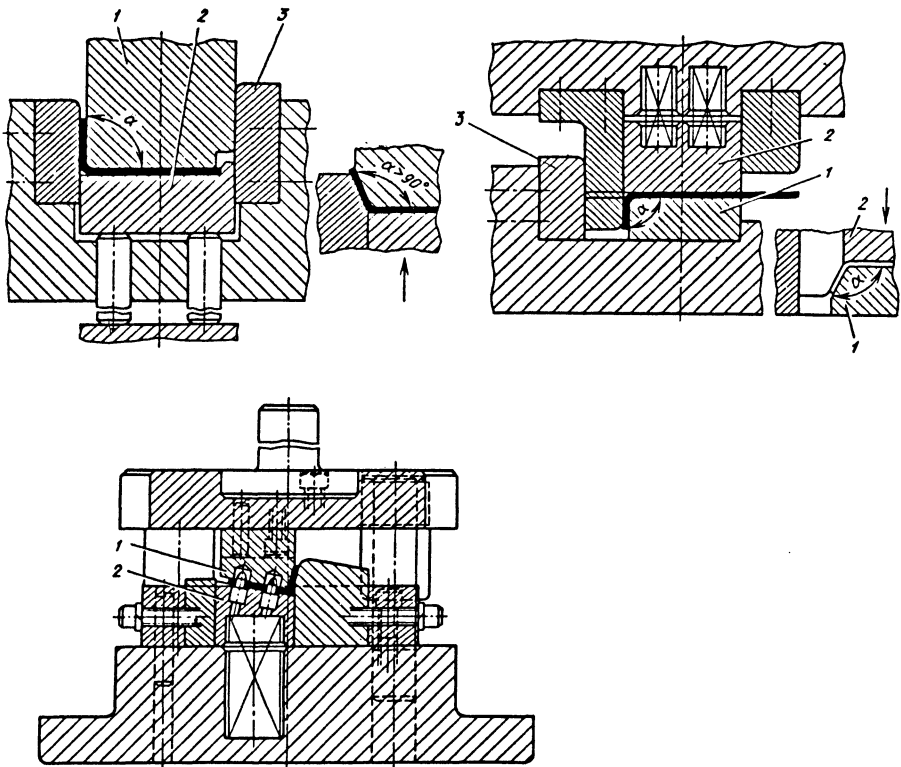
Г-образная гибка с защемлением одной полки штампуемой детали
